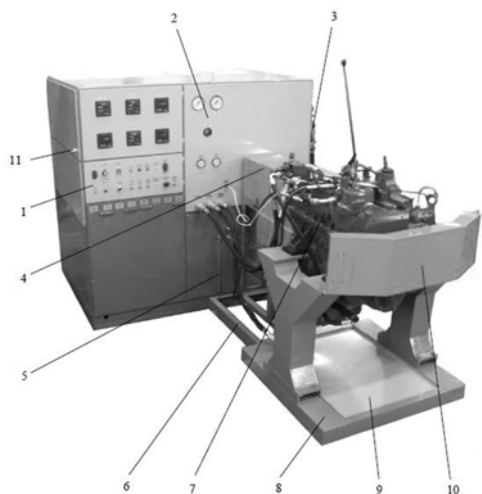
Общий вид стенда для обкатки коробок перемены передач тракторов «Кировец»
